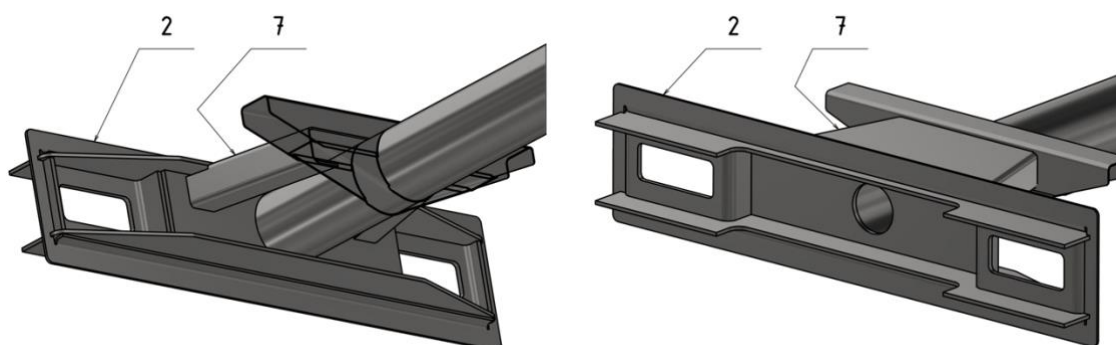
Detailní pohled pozice č. 3
